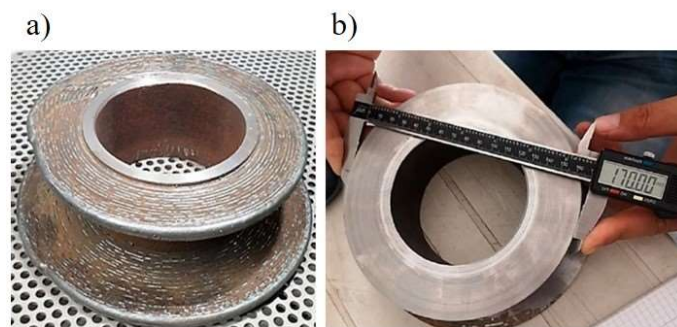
17 Pièce fabriquée par Feier et al. [71] : a) Avant usinage b) Après usinage.
